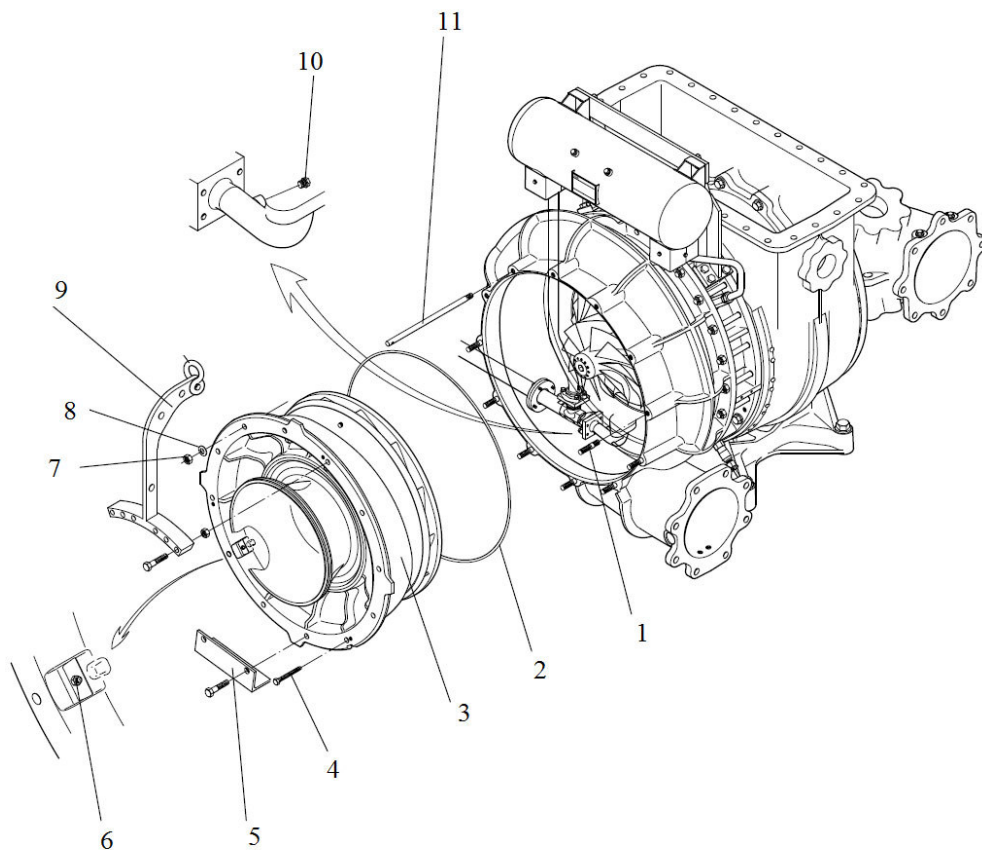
Демонтаж внутрішньої частини корпусу компресора:
